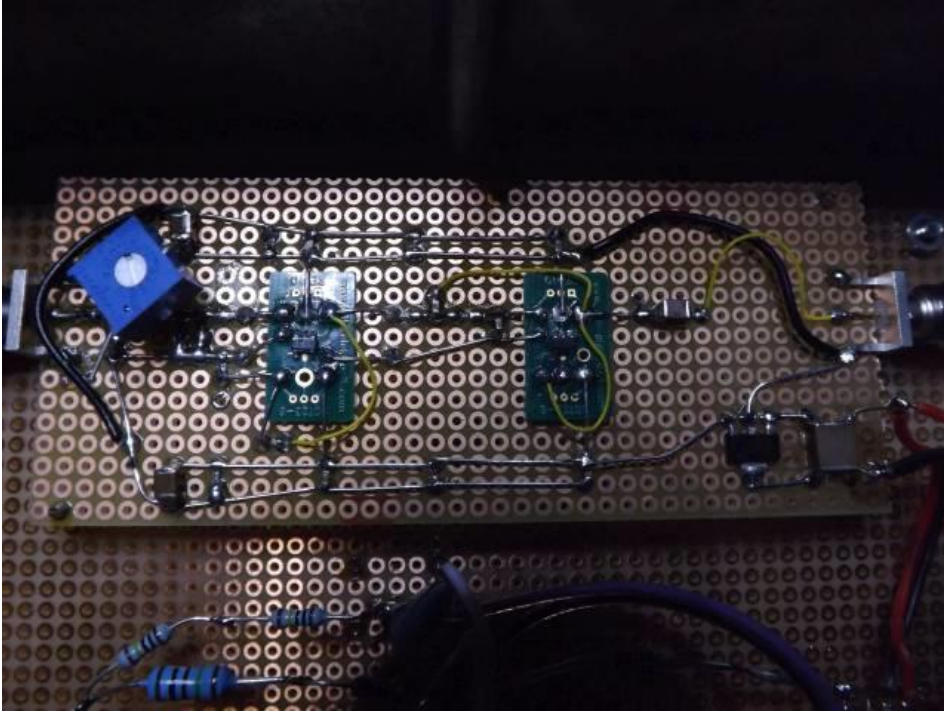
Detailaufnahme des Impulsformers aufgebaut als Prototyp mit 0603 SMT Bauteilen auf Lochraster und OPs auf Adapterplatinen der Firma Rohm
